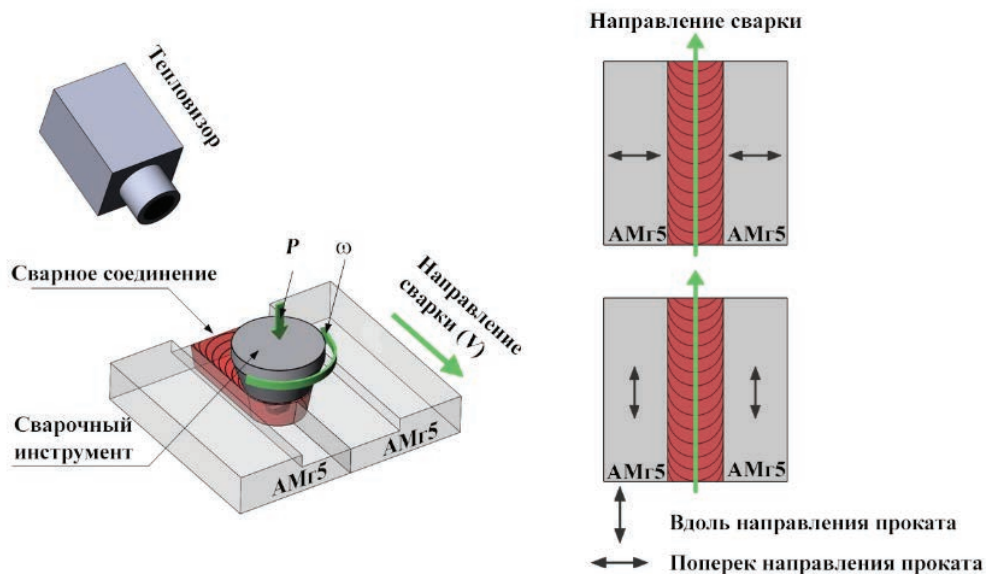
Схема процесса сварки трением с перемешиванием
